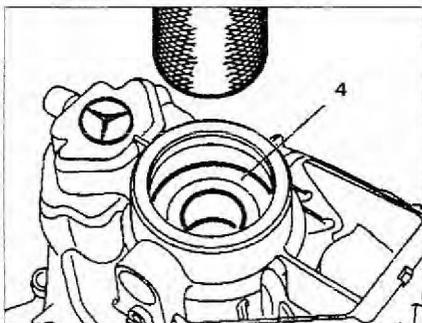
Выпрессуйте подшипник 4 вторичного вала.
